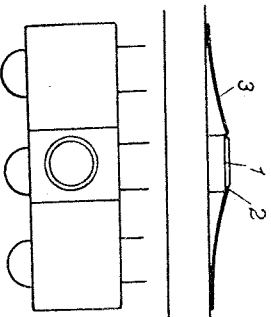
Upnutí na otočném stole s magnetickou deskou
